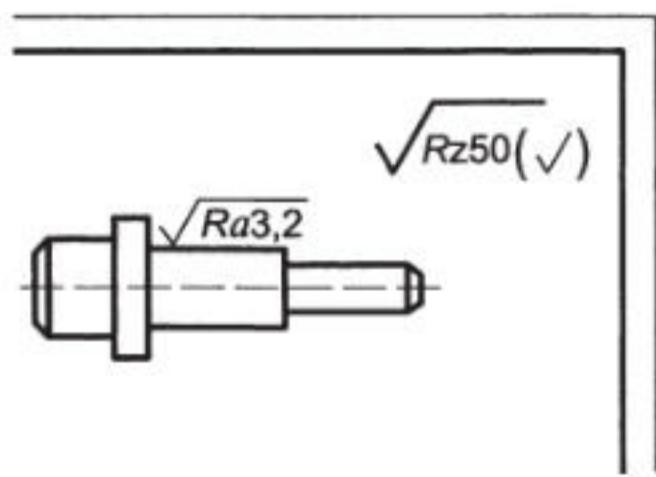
Обозначение шероховатости, одинаковой для части поверхностей изделия
